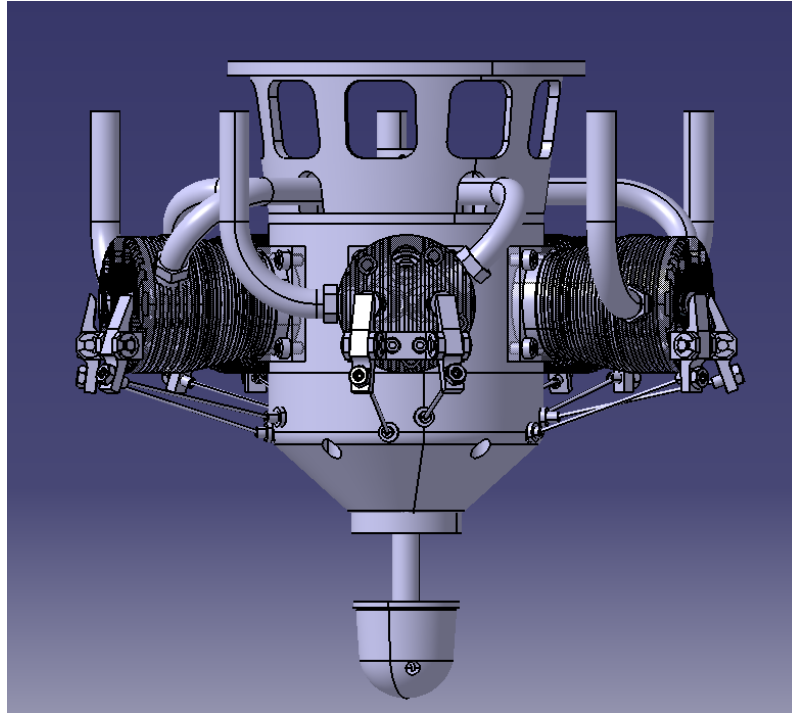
Vista en planta del ensamblaje final en Catia V5.
